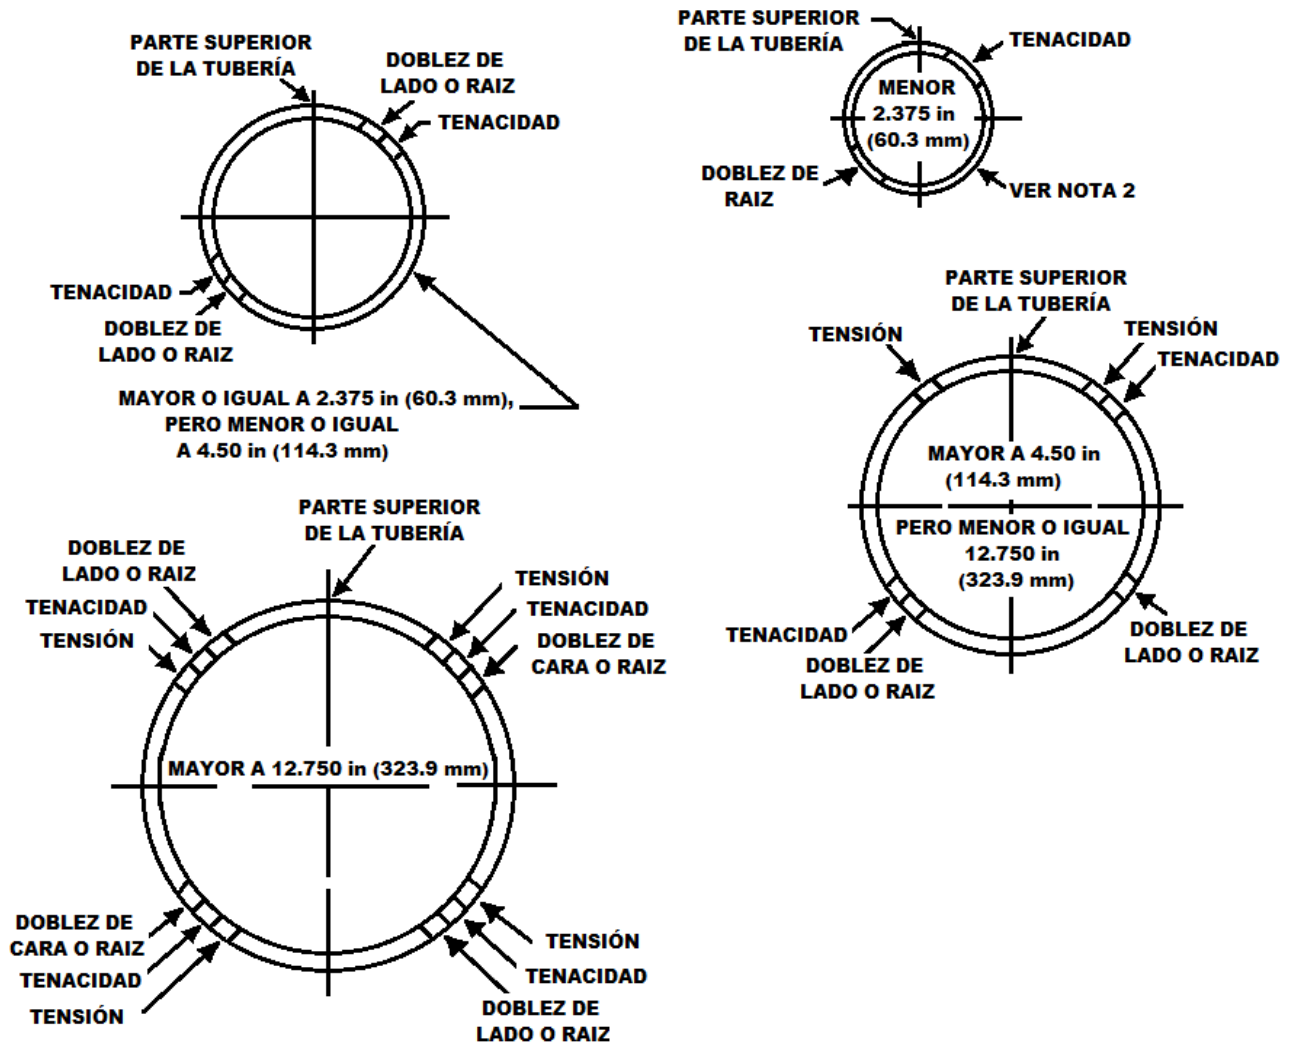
Localización de las probetas para calificar soldadores según API 1104 (122)
